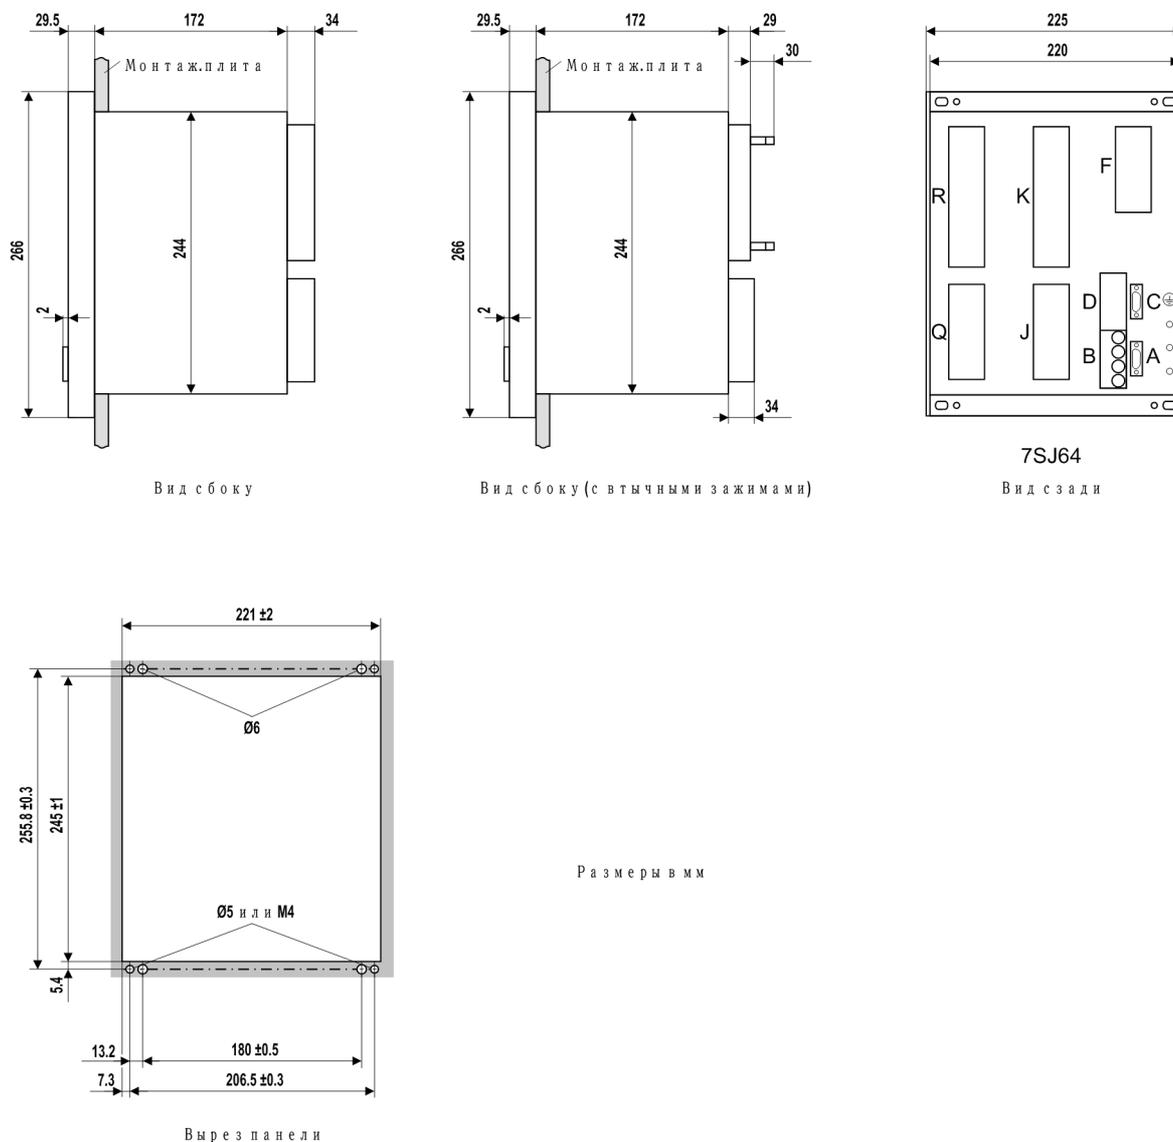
Размерный чертеж устройства 7SJ64 для утопленного монтажа на панели и в шкафу (размер корпуса 1/2)
